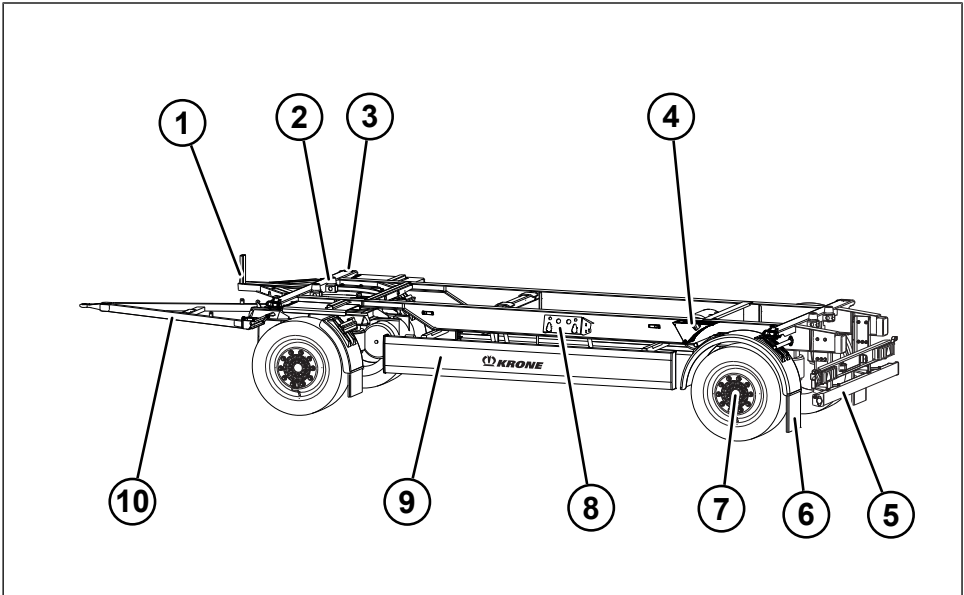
Übersicht Box Carrier Drehschemelausführung (2-Achser)
